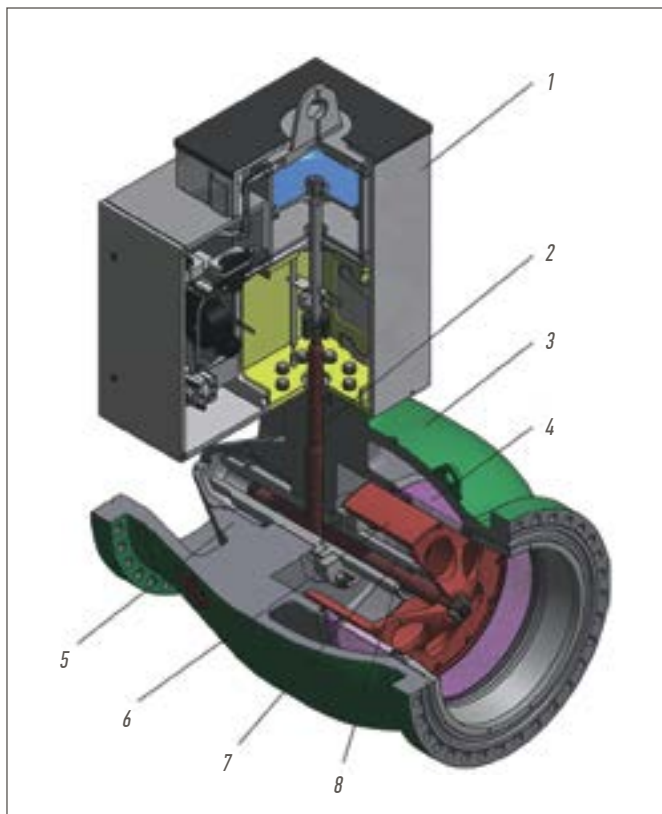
Клапан регулирующий антипомпажный: 1 – пневмопривод; 2 – шпindelь; 3 – корпус; 4 – сепаратор; 5 – обтекатель; 6 – поршень; 7 – втулка; 8 – шток
